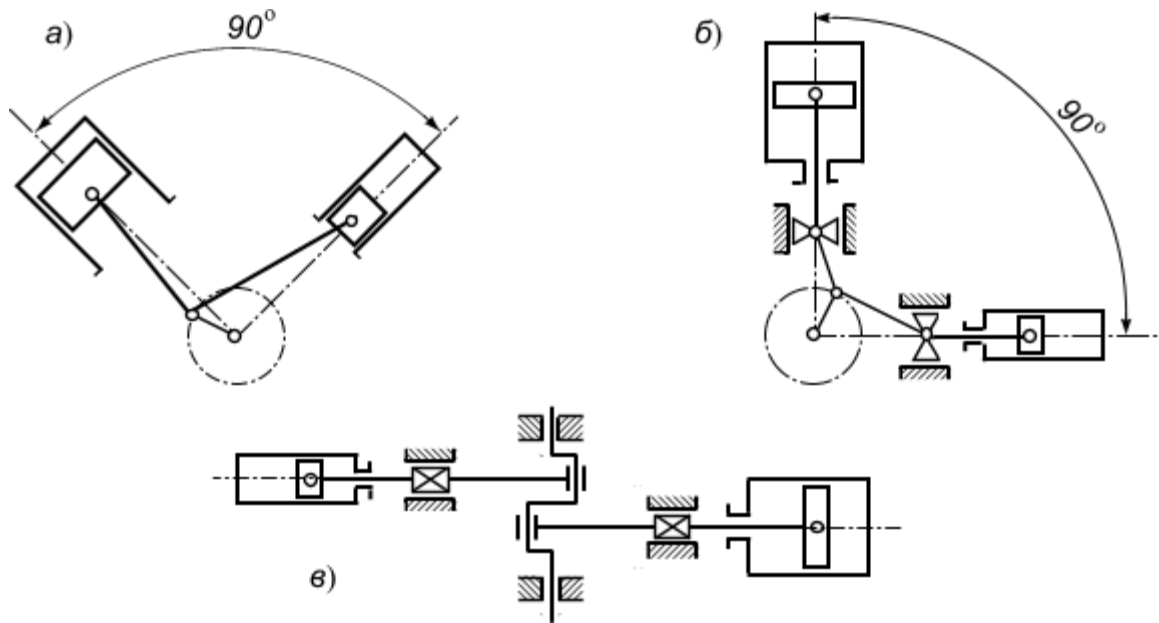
Кинематические схемы поршневых компрессоров применяемых в системах воздухообеспечения: а – воздушный бескрейцкопфный компрессор с V-образным расположением цилиндров (ВУ); б – воздушный кресткопфный с прямоугольным расположением цилиндров (ВП); в – воздушный кресткопфный с горизонтальным оппозитным расположением цилиндров (ВМ).
